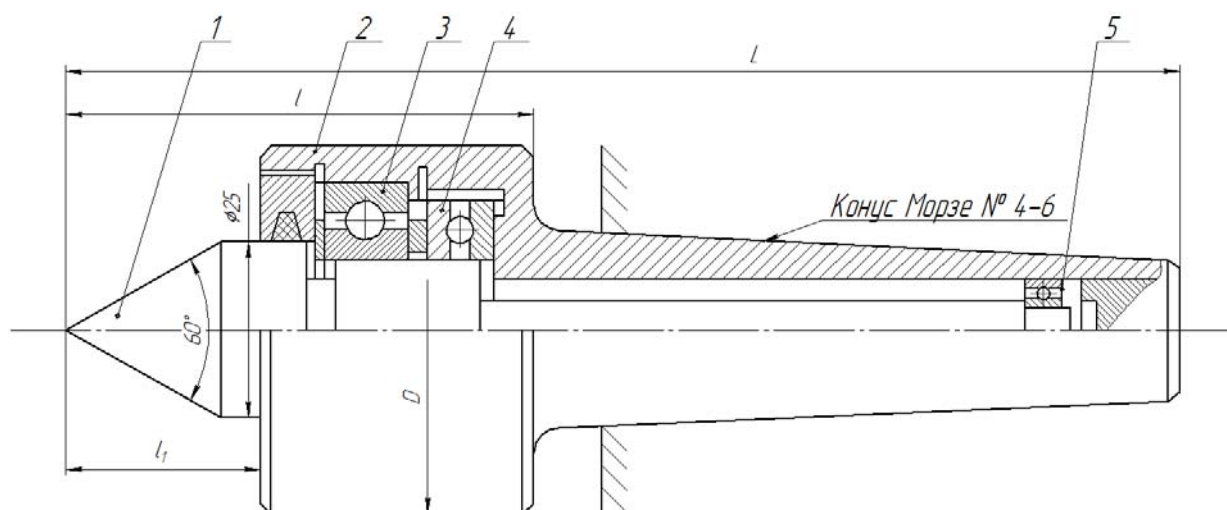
Будова обертвого центра для центрованих деталей: 1 – центр; 2 – корпус; 3, 5 – радіальний підшипник; 4 – упорний підшипник
